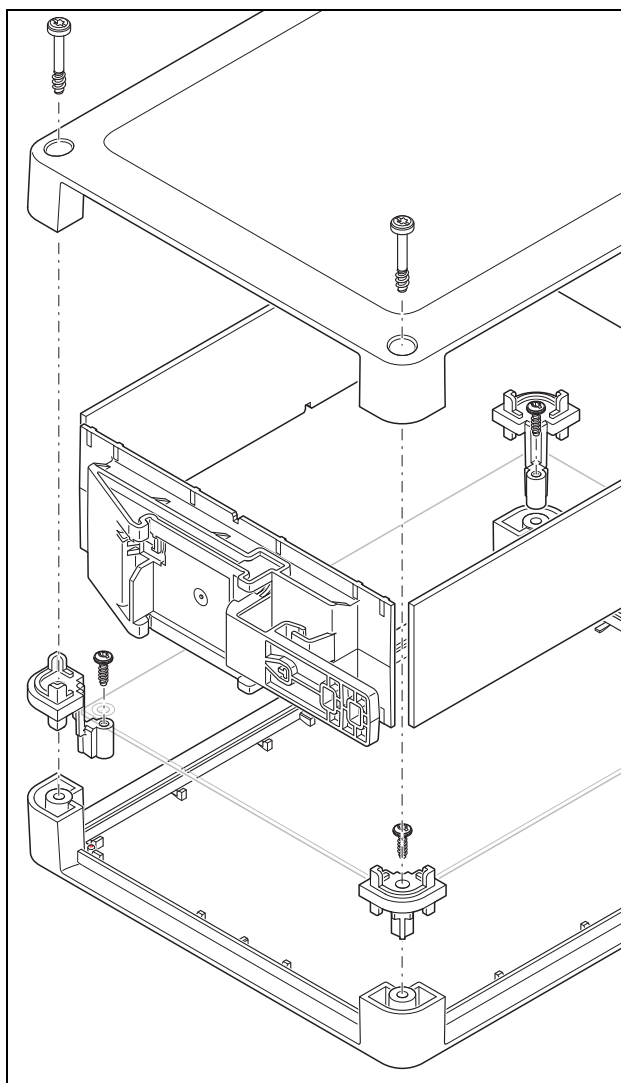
Gehäuse mit Tragschienenadapter (Beispiel)
